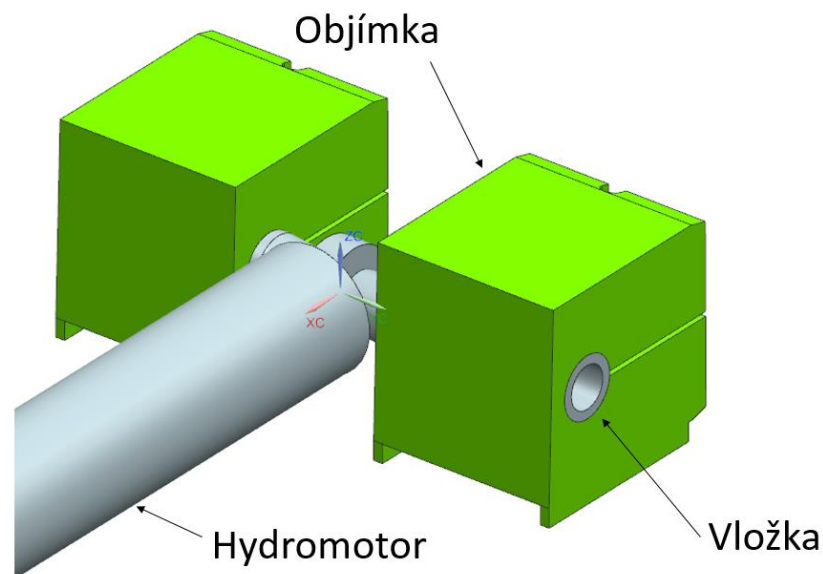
Upevnění testovaných hydromotorů – zadní pohled
